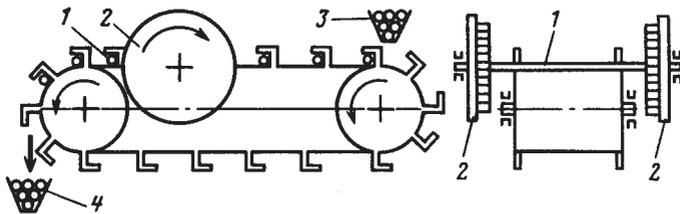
Схема механизма зачистки труб металлическими щетками:
